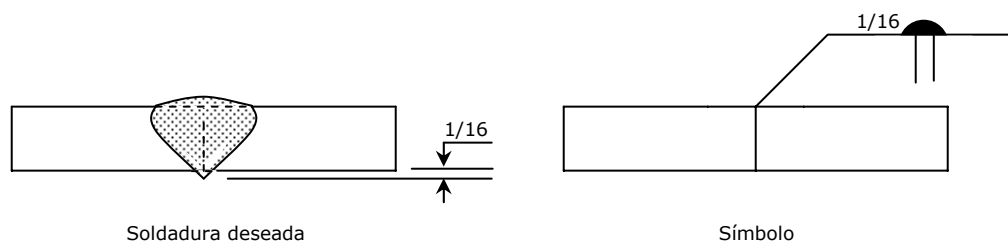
Símbolo de soldadura de penetración
